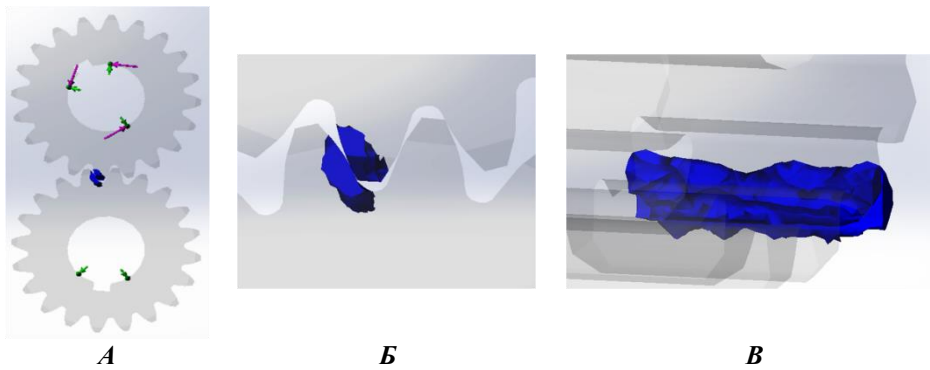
Контуры нагруженности зубьев ведущего и ведомого колес: *A* – главный вид зубчатой передачи; *Б* – увеличение в месте зацепления; *В* – разрез места зацепления.
